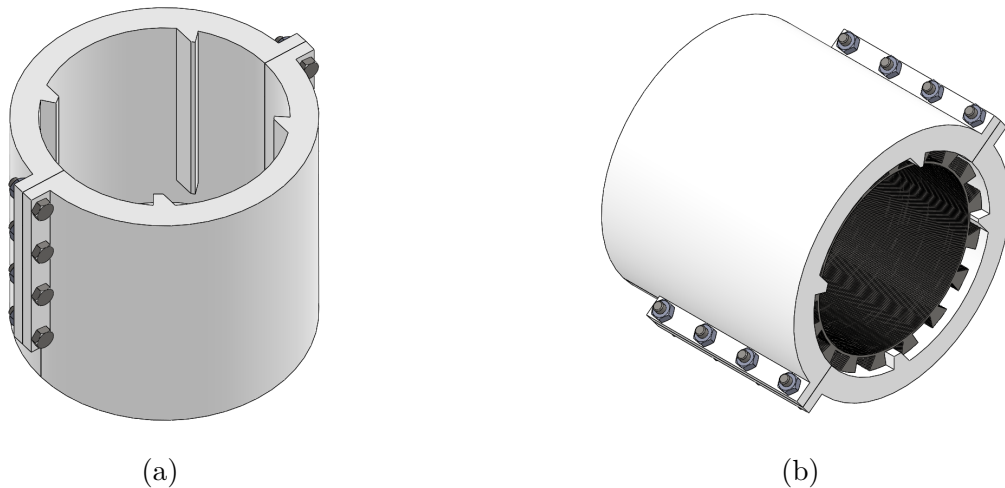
Outil d’assemblage des tôles du rotor basse vitesse : (a) outil (b) outil monté
